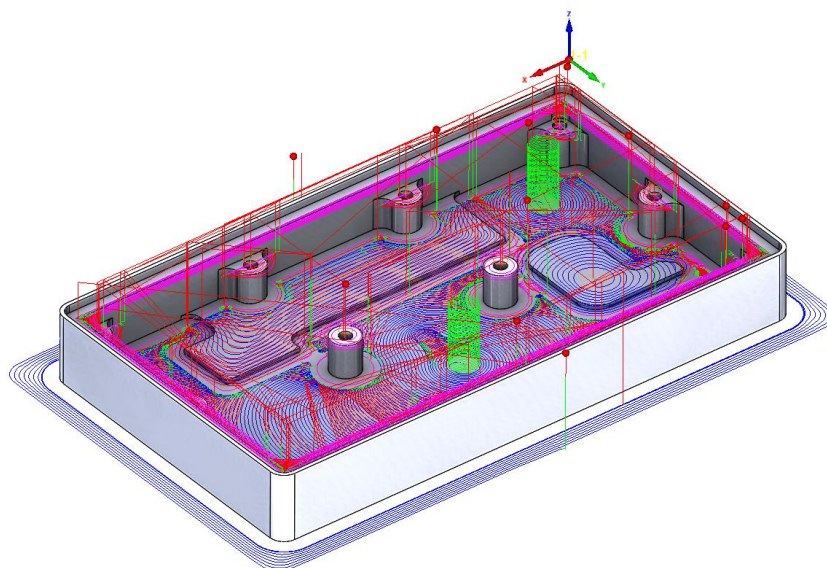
Динамическое трохоидальное фрезерование детали типа «Корпус»
